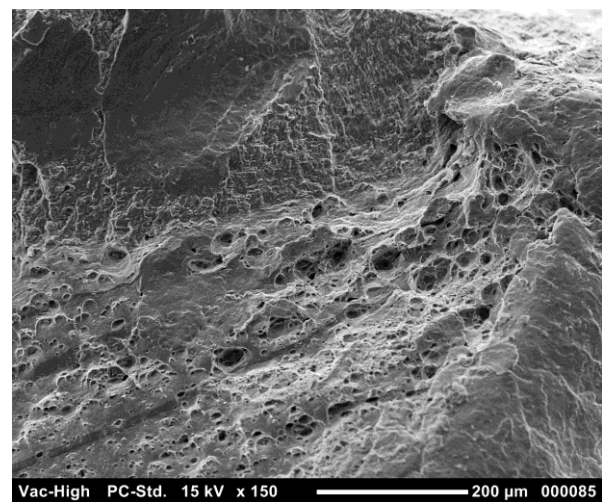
Übersichtsaufnahme der Bruchoberfläche einer Schweißung des Parametersatzes IMWF-33-00020 ($n=1500 \text{ min}^{-1}$, $v_x=500 \text{ mm/min}$)
